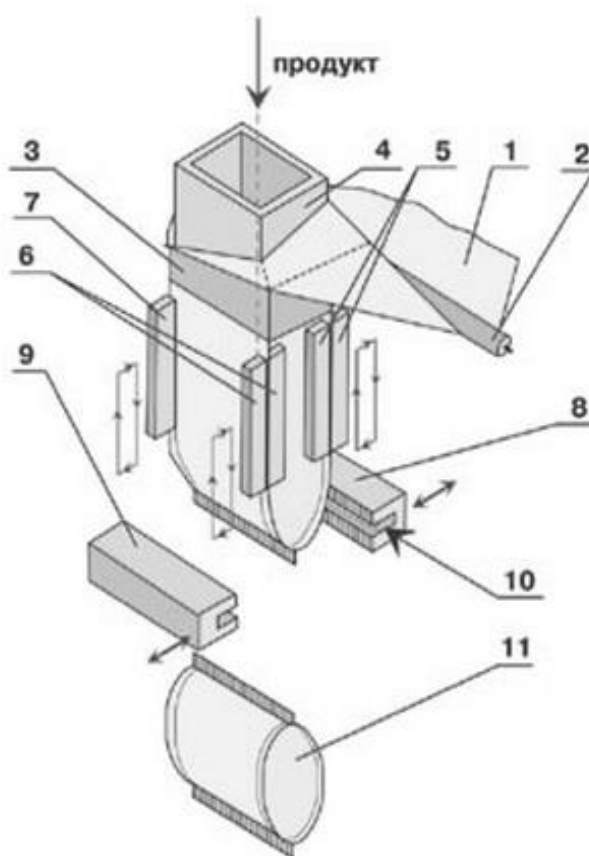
Схема машини з комірцем періодичної дії з протягуючими губками поздовжнього шва зварювання: 1 – пакувальний матеріал; 2 – напрямний ролик; 3 – комірцев; 4 – прямокутний трубопровід; 5, 6, 7 – поздовжні зварювальні губки; 8, 9 – поперечні зварні головки; 10 – ніж; 11 – готова упаковка.
